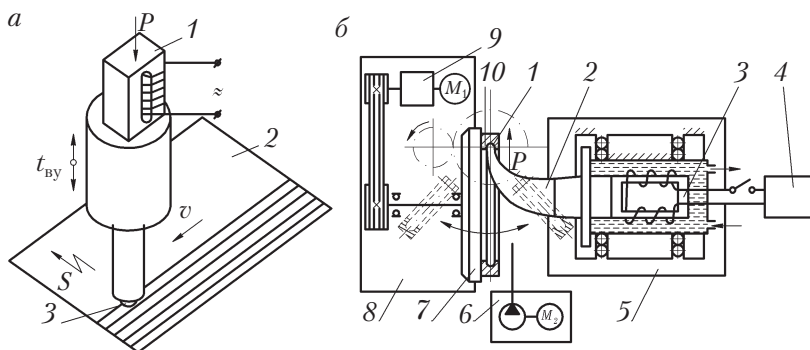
Рабочая зона установки для ультразвукового ППД на базе поперечно-строгального станка мод. 7Е35 (*а*) и схема установки для ультразвукового выглаживания желоба наружных колец шарикоподшипников на базе желобошлифовального станка ЛЗ-29П (*б*)
